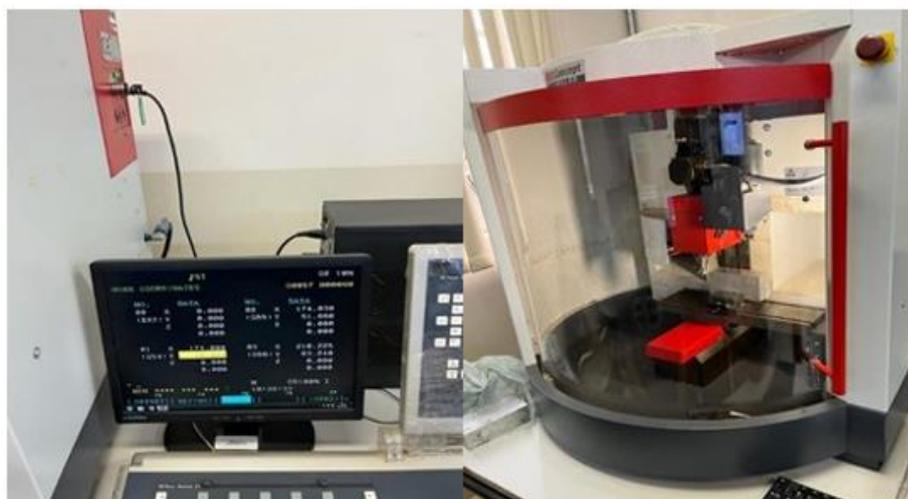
Desenvolvendo a programação para a usinagem do molde e testes para a usinagem do molde no centro de usinagem CNC.
